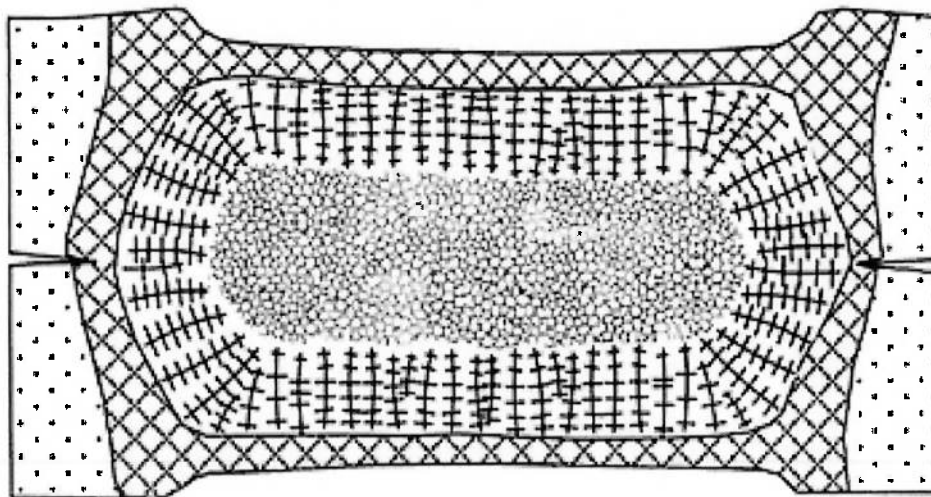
Ponto de solda desejável, resfriamento uniforme [14].
